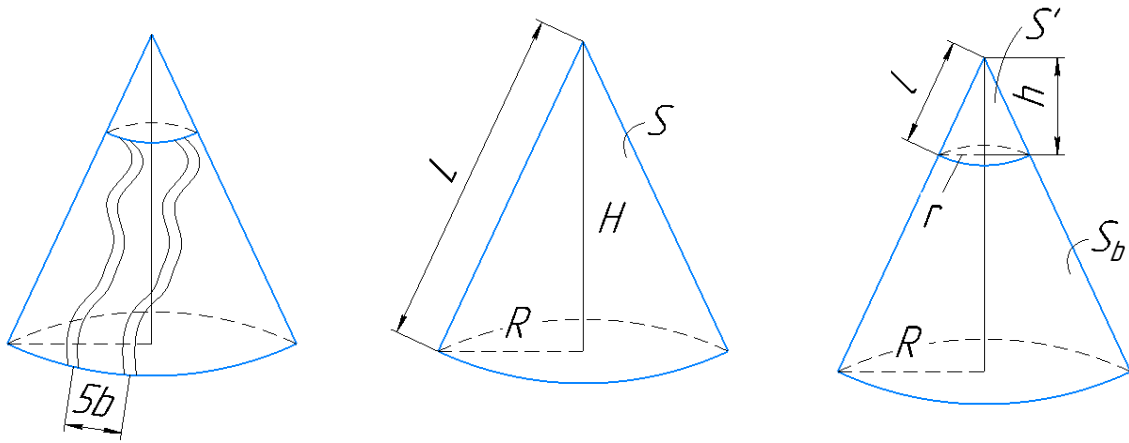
Конусна деталь механізму тиску з мікрорельєфом.
